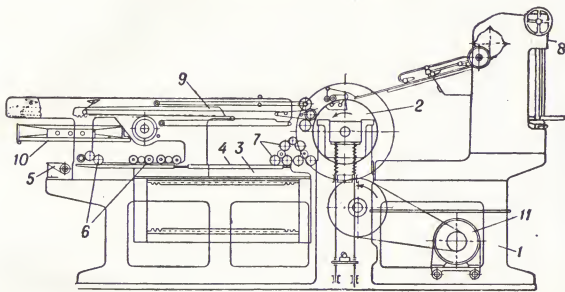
Схема двухоборотной плоскочечатной машины: 1 — станина; 2 — печатный цилиндр; 3 — талер; 4 — печатная форма; 5 — красочный ящик; 6 — раскатная система красочного аппарата; 7 — накатная система красочного аппарата; 8 — самонаклад для бумаги; 9 — транспортёр готовых оттисков; 10 — приёмный стол для оттисков; 11 — электродвигатель.
